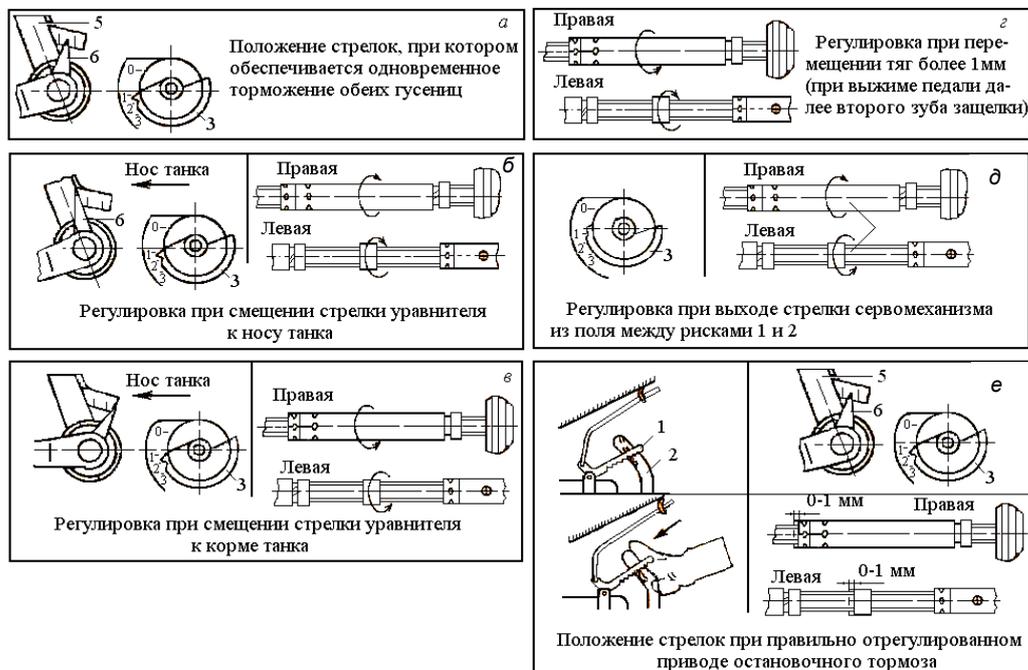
Регулировка привода остановочного тормоза (положения деталей привода при регулировке):
